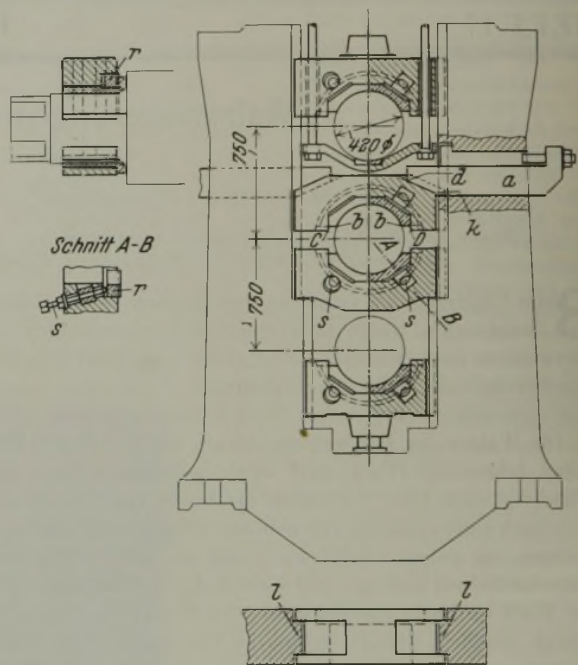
Einbau und Walzenlagerung der 750er Trio-Blockstraße.
